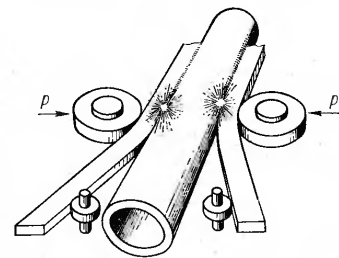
Схема высокочастотной сварки плавниковых труб
